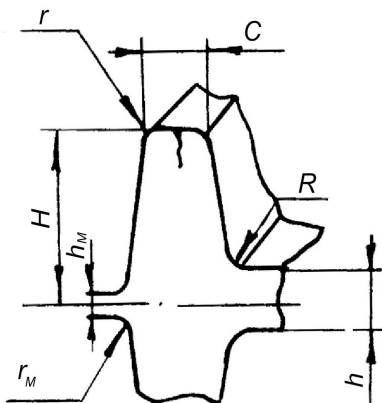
Характерний дефект виготовлення штампованих поковок
